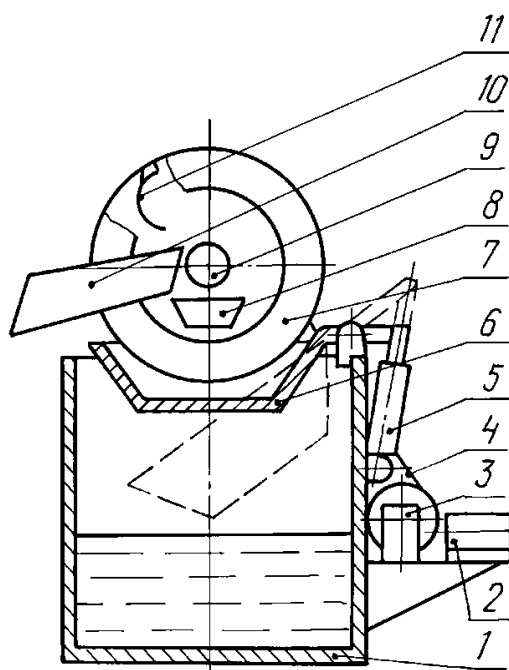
Установка для очистки металлических изделий (метизов): 1 – ванна; 2 – электродвигатель; 3 – редуктор; 4 – передача цепная; 5 – пневмоцилиндр; 6 – ванна подвижная; 7 – барабан перфорированный; 8 и 10 – лотки; 9 – гидрант; 11 – пластина разгрузочная
